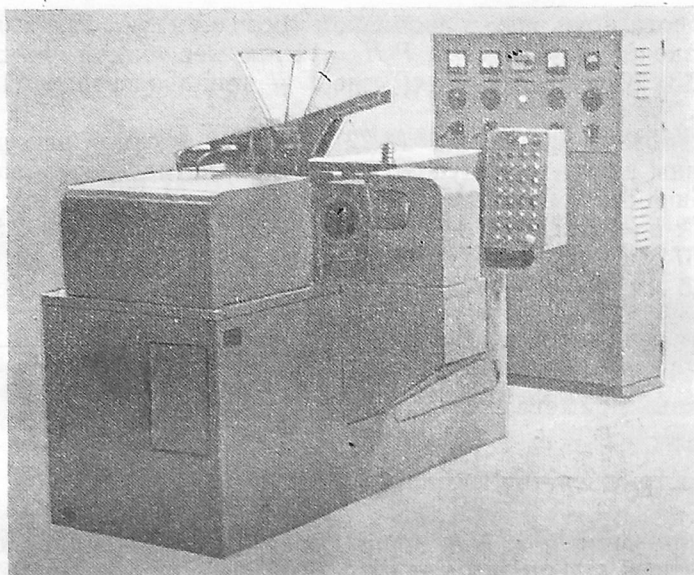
Общий вид экспериментального станка-автомата мод. ФАС-1 для обработки колец, втулок и других деталей на оправке
